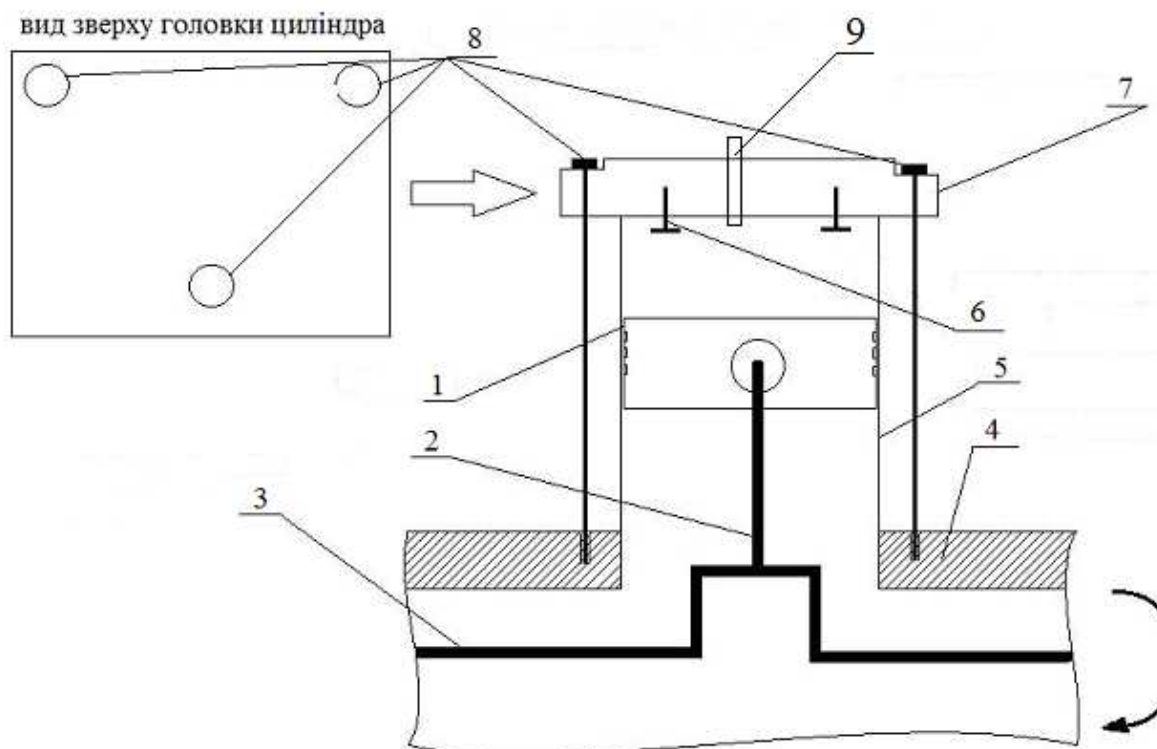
Схема закріплення головки циліндра до картера двигуна: 1 – поршень; 2 – шатун; 3 – колінчастий вал; 4 – блок картера; 5 – гільза циліндра; 6 – впускний та випускний клапани; 7 – головка циліндра; 8 – болти з'єднання головки циліндра та блока; 9 – форсунка
